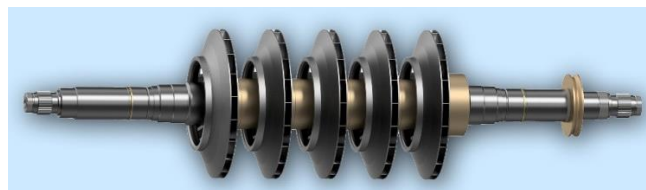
Загальний вигляд ротора відцентрового вакуум-компресора
